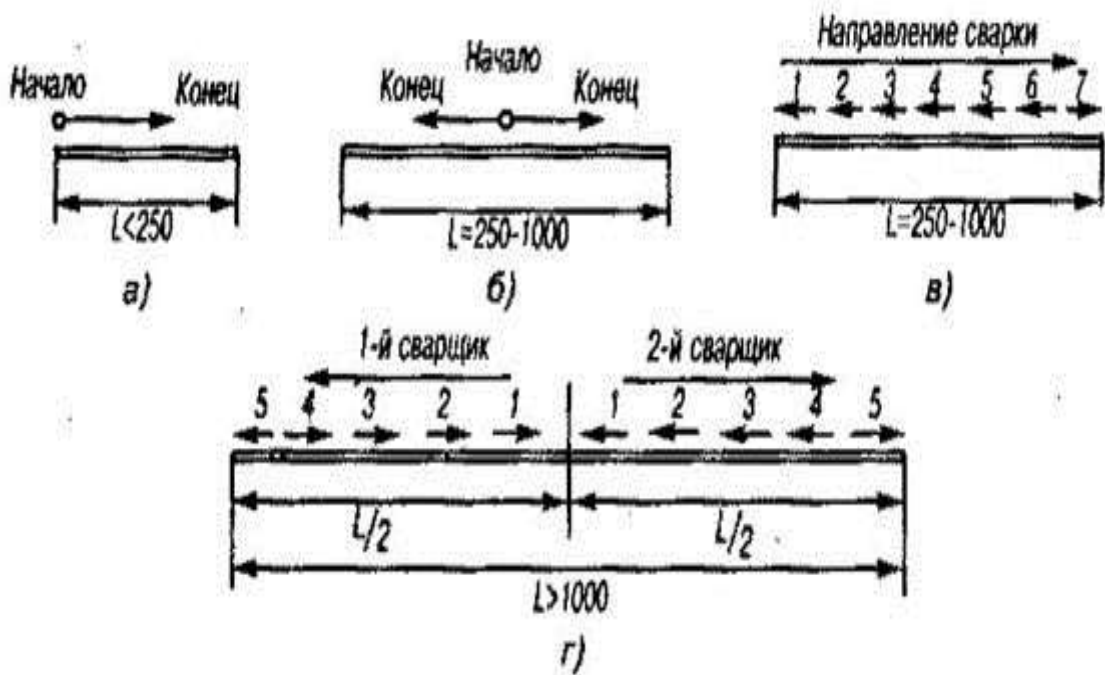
Выполнение сварных швов различной длины.
